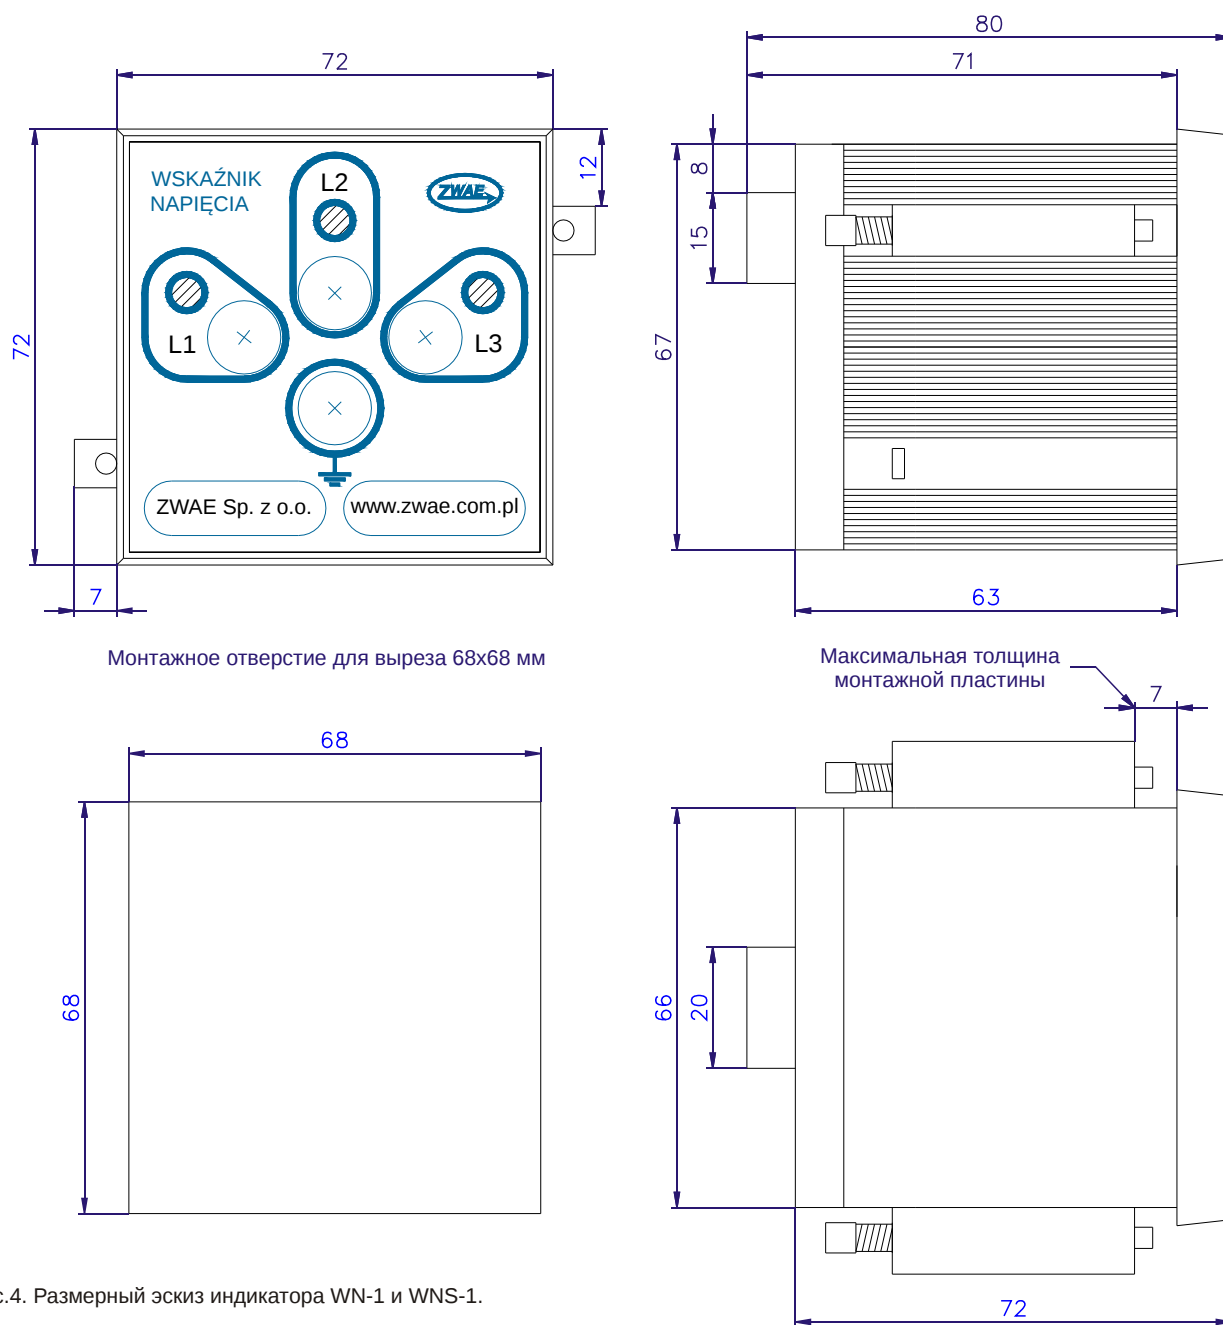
Размерный эскиз индикатора WN-1 и WNS-1.
